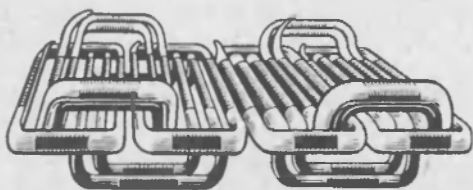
Вариант расположения лобовых частей однослойной обмотки
